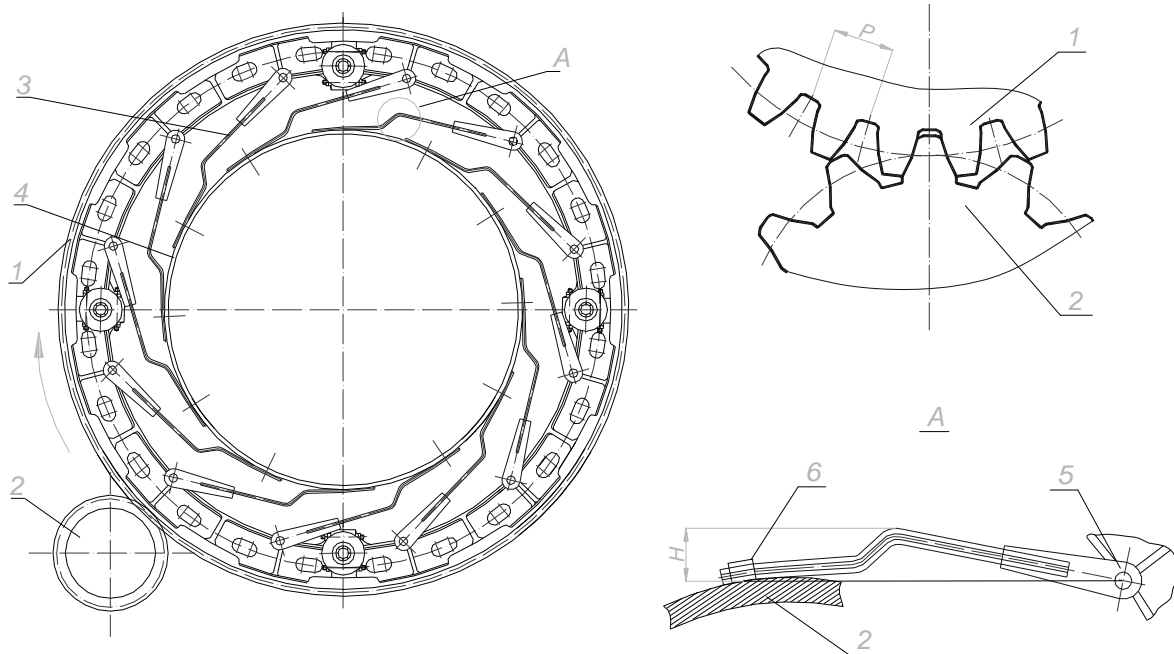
Вузол з'єднання вінцевої шестерні з корпусом обертової печі
